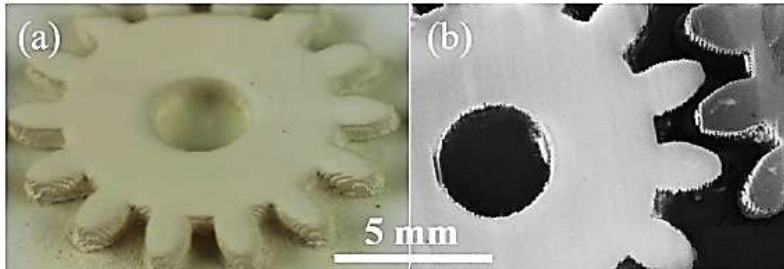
Зубчасте колесо Si_3N_4 , виготовлене ІР методом:
